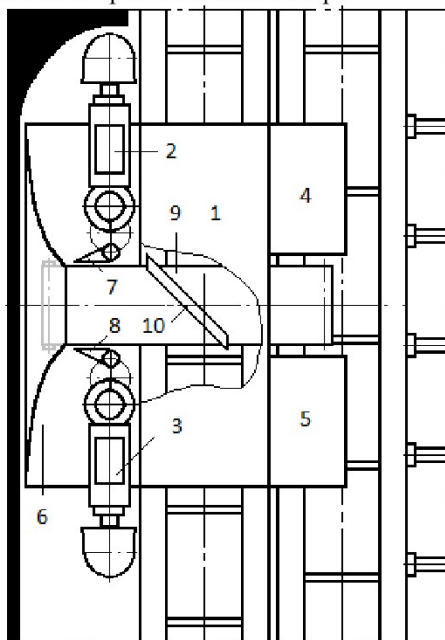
Очистной комбайн для селективной выемки угольного пласта сложного строения (вид в плане): 1 – корпус; 2, 3 – режущий исполнительный орган избирательного действия; 4, 5 – площадка; 6 – лоток; 7, 8 – нагребающая лапа; 9 – ленточный перегружатель; 10 – плужковый сбрасыватель
